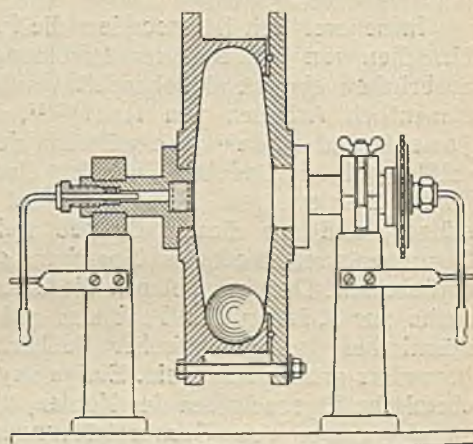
Neue Ausführung der Vakuumkugelmühle.
